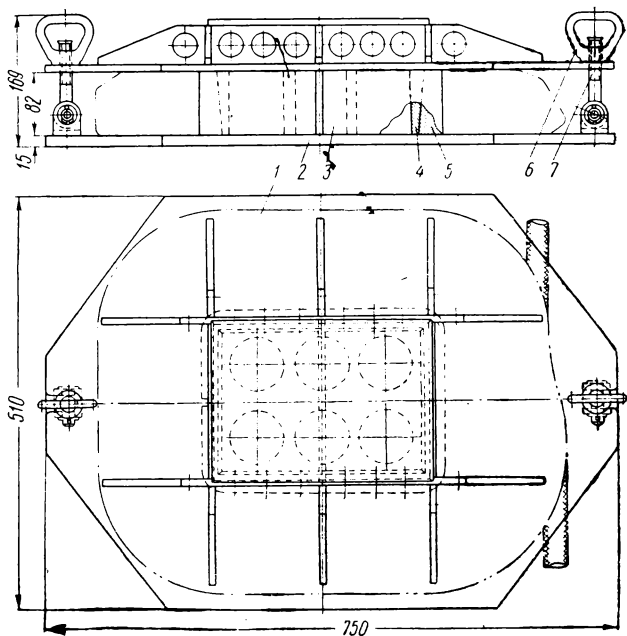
Приспособление для опрессовки катушек главных полюсов тяговых двигателей:
